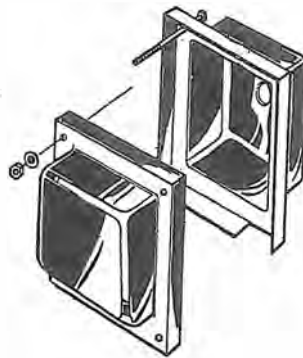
Q - Le calotte conferiscono migliore estetica, protezione degli avvolgimenti e schermatura. Sono spesso assai rigide, sì da fungere anche da serrapacco.
